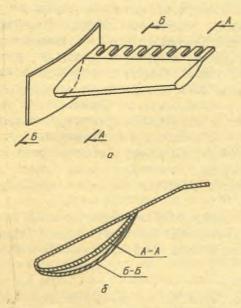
Лопасть новой транспортной системы: а - общий вид; б - поперечные сечения лопасти
